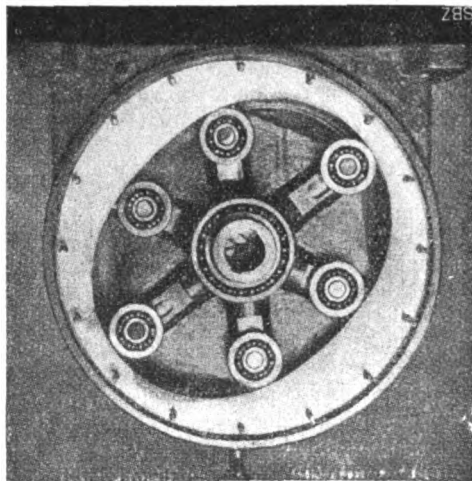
Moteur de transmission Hele Shaw. Vue de côté, couvercle enlevé.
